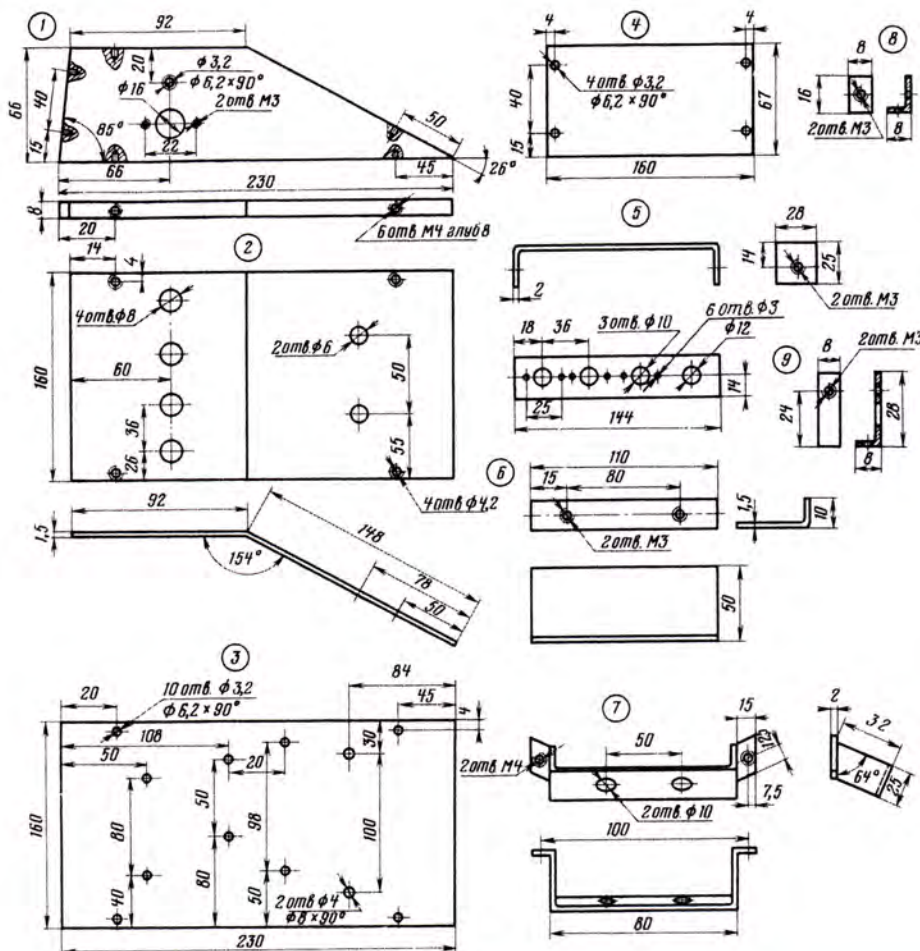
Детали корпуса приставки. 1 — боковая стенка, гетинакс, 2 шт.; 2 — верхняя крышка, дюралюминий Д16АТ; 3 — дно, дюралюминий АМГ; 4 — задняя крышка, дюралюминий АМГ; 5 — скоба, дюралюминий АМГ; 6 — перегородка, дюралюминий АМГ; 7 — кронштейн, сталь 10; 8, 9 — уголки крепления плат, 2 шт., дюралюминий АМГ.
